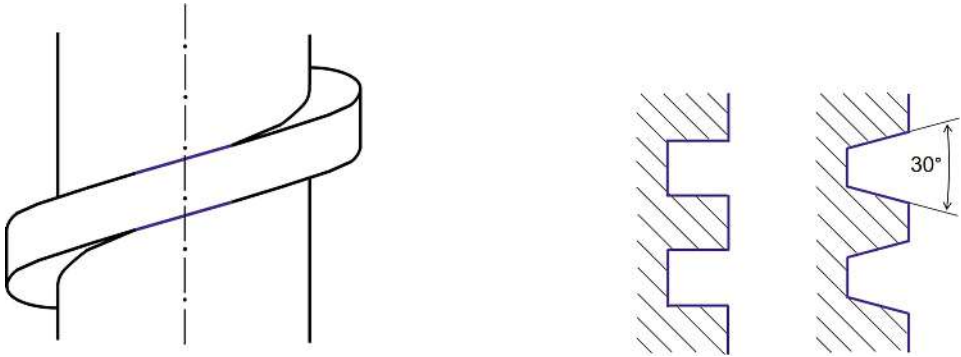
Flachgewinde (links), Gewindeprofile (rechts)
